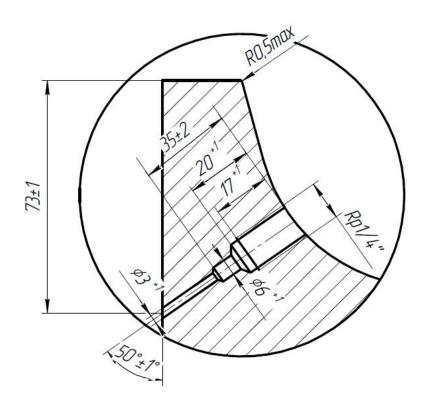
Масленочное отверстие колеса Ø 750 мм ( ссылочный № 29240, ред. Е )
